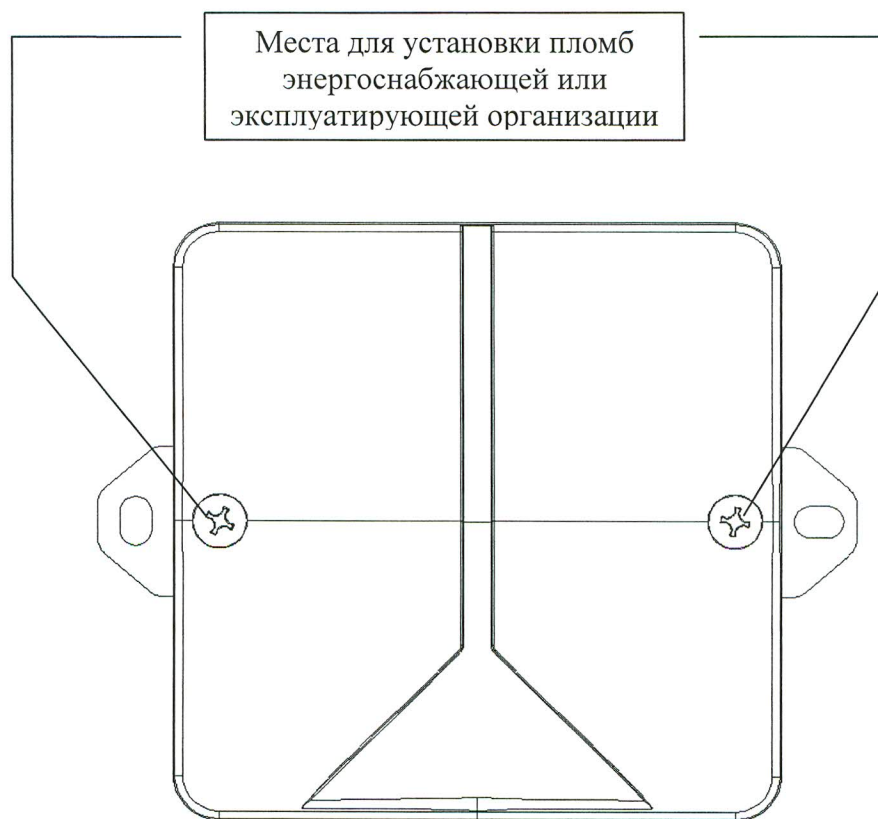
Схема пломбировки сумматора СЕ826-02
